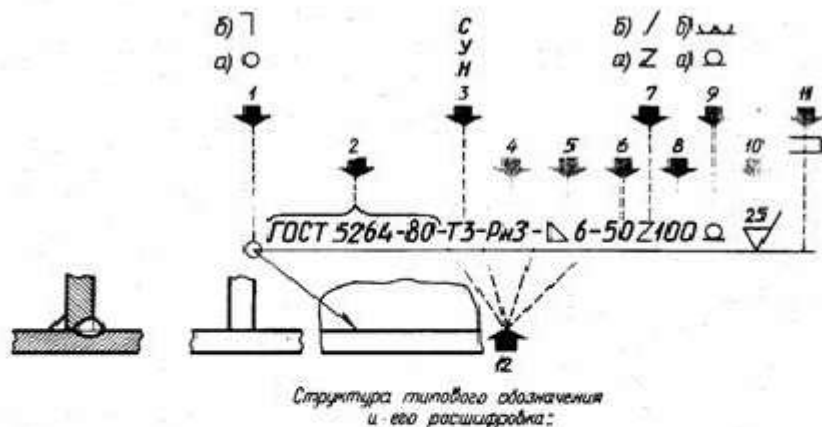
Структура обозначения шва сварного соединения (сварка плавлением):
